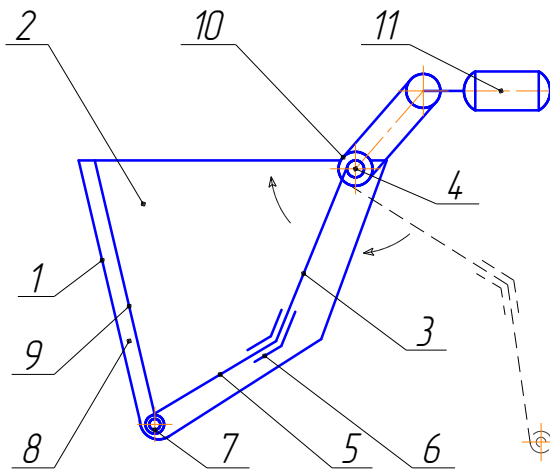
Кормушка для животных 1 – Передняя стенка; 2 – боковые стенки; 3 – верхняя часть лопатки; 4 – ось; 5 – нижняя часть лопатки; 6 – гибкая связь; 7 – боковые стенки; 8 – пазы; 9 – направляющие; 10 – подшипники; 11 – механизм привода для поворота лопатки;
